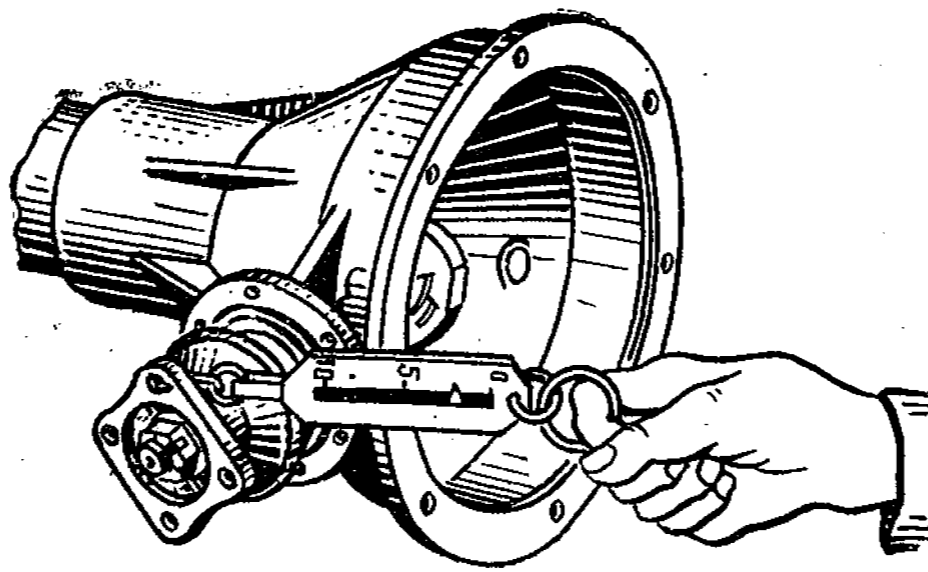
Проверка затяжки конического подшипника ведущей шестерни
